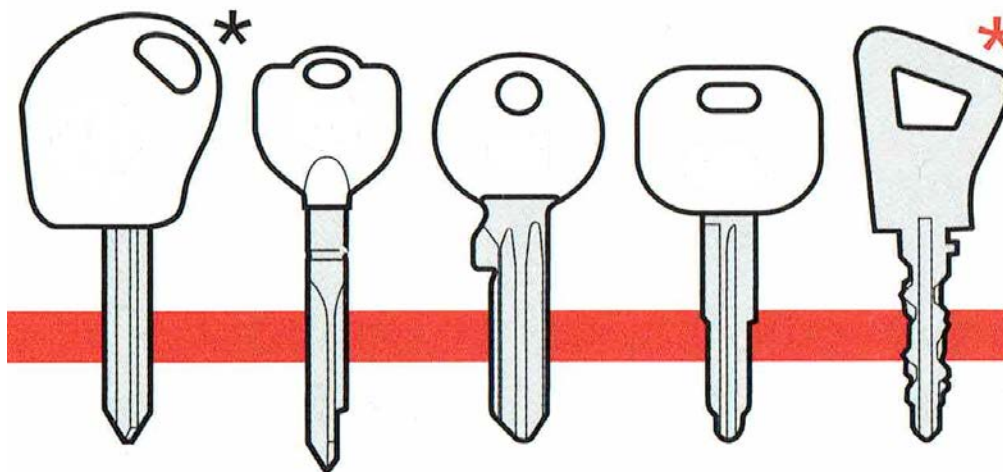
les clés plates et en croix usiner par la machine KEYLINE CARAT.
